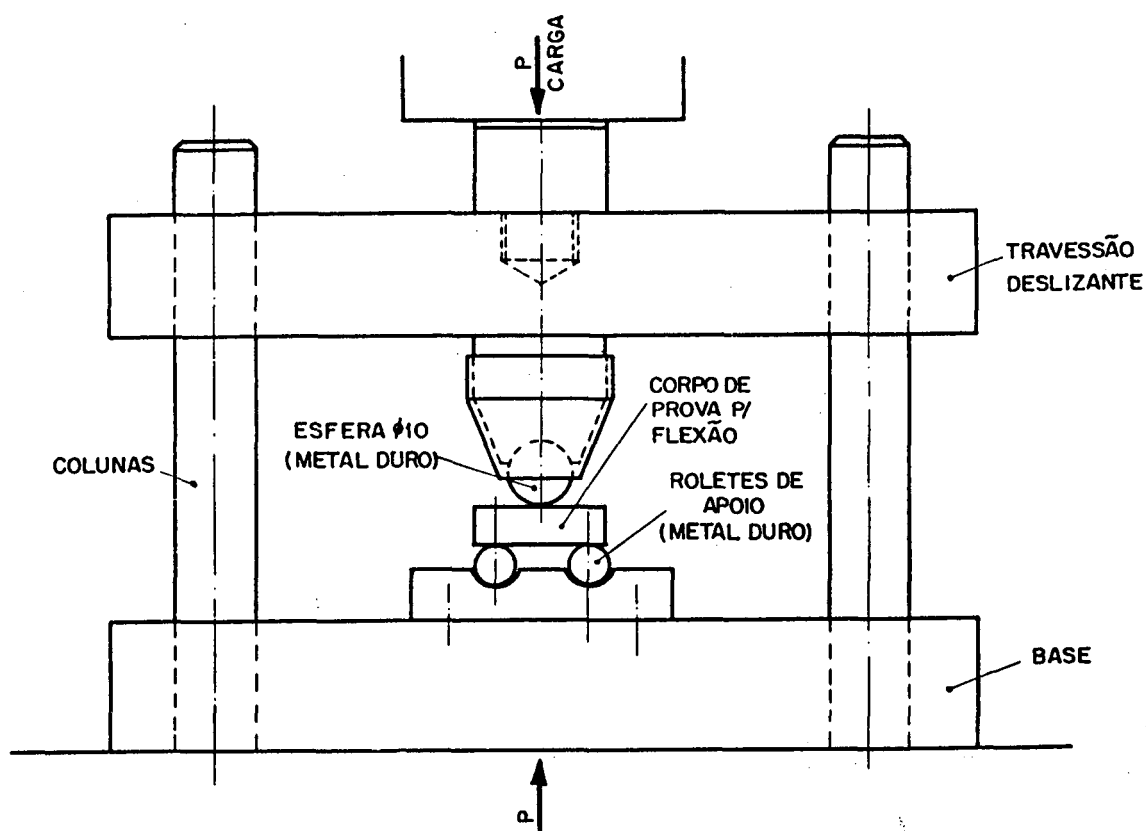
Dispositivo usado para ensaios de flexão (ASTM-B-406-76).
